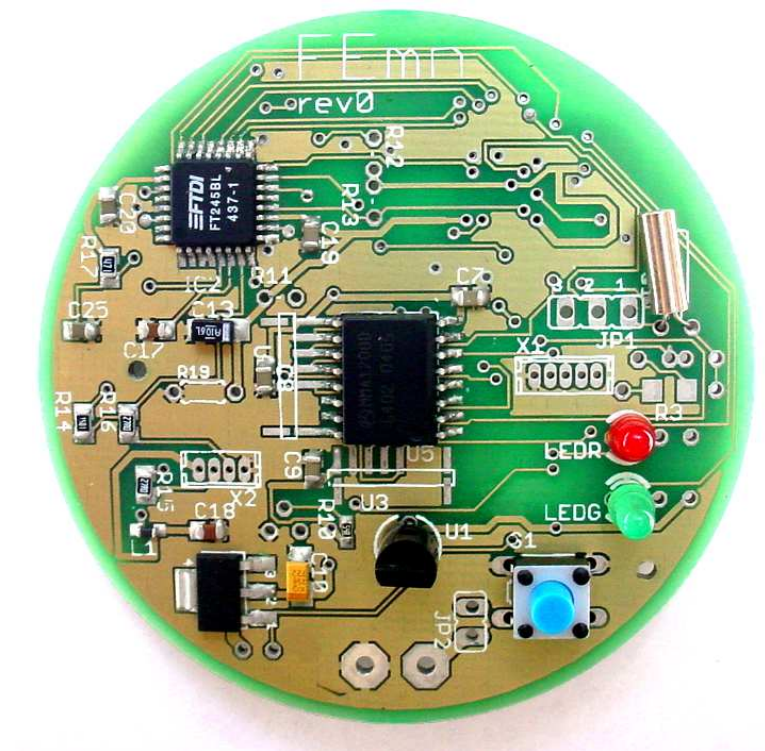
Foto da PCB do segundo protótipo da FE com os componentes eletrônicos.
